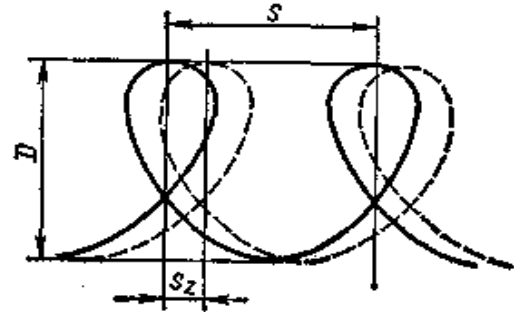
Траєкторія руху інструменту при фрезеруванні
